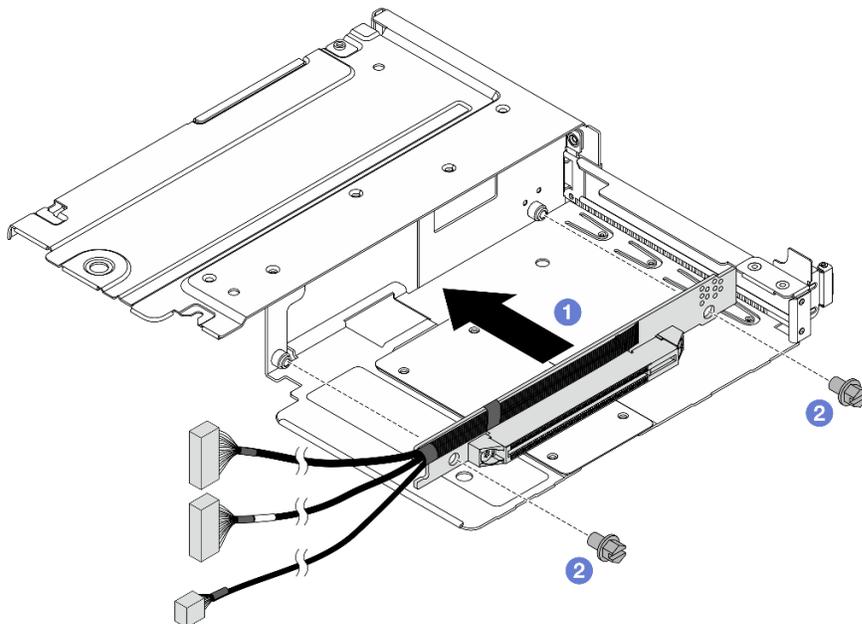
Installation de la carte mezzanine dans un boîtier pleine hauteur
